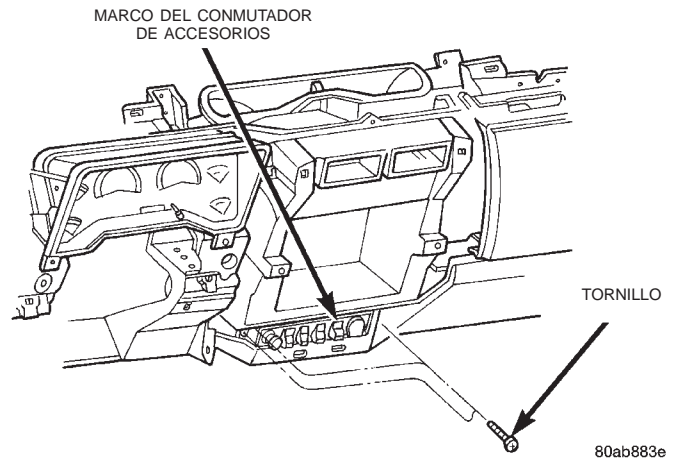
Desmontaje e instalación del marco del conmutador de accesorios
